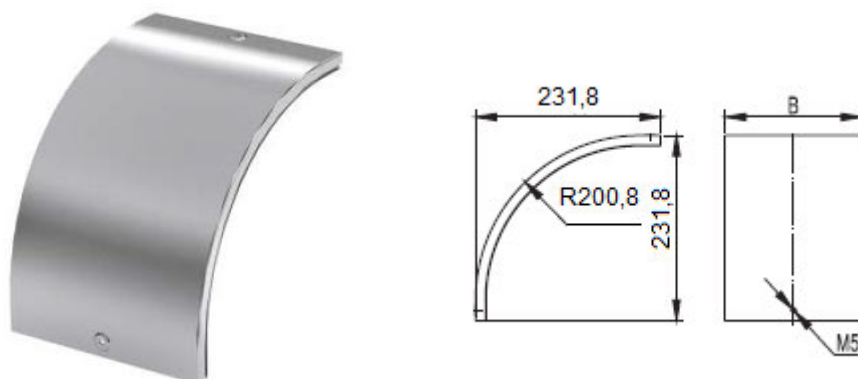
Крышка CD 90 на угол вертикальный внешний 90°, тип 3824
